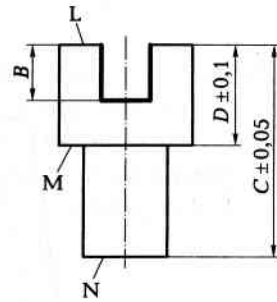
Эскиз обрабатываемой детали к заданию 1.33
